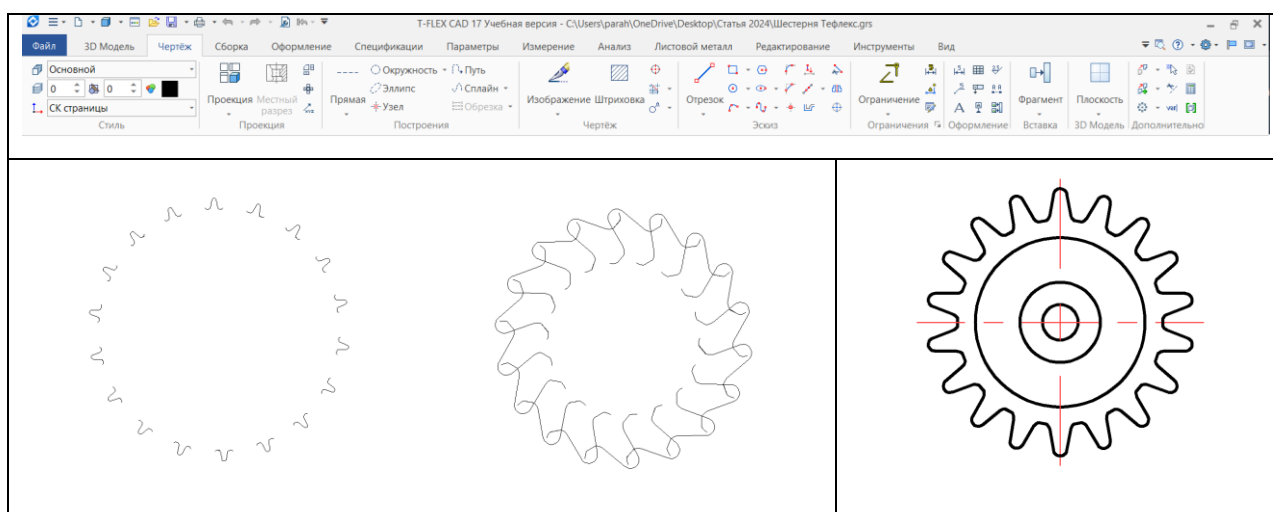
Изображение шестерни (зубчатая передача) в T-FLEX CAD
